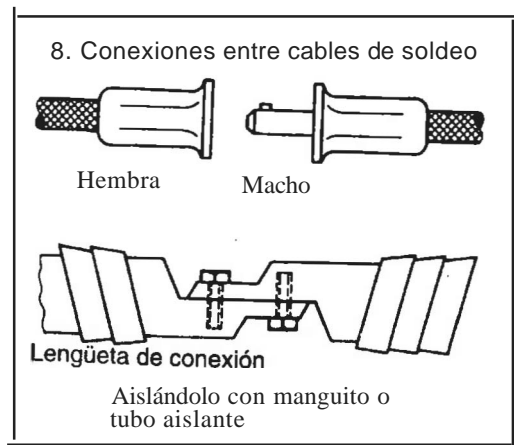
CONEXIONES PARA CABLES DE SOLDEO
